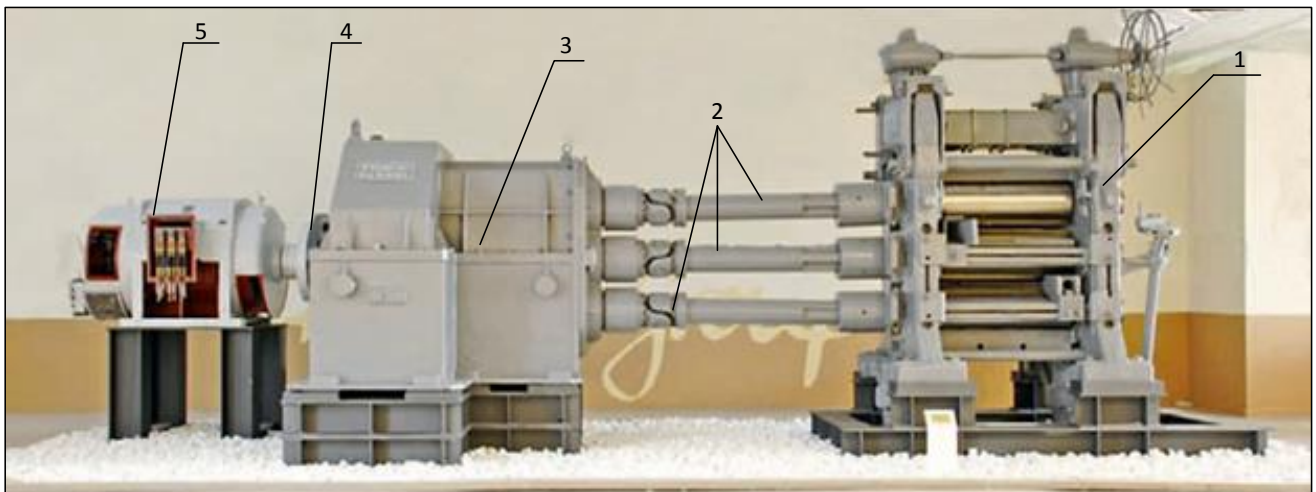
Внешний вид рабочей линии 3-х валковой клетки:
